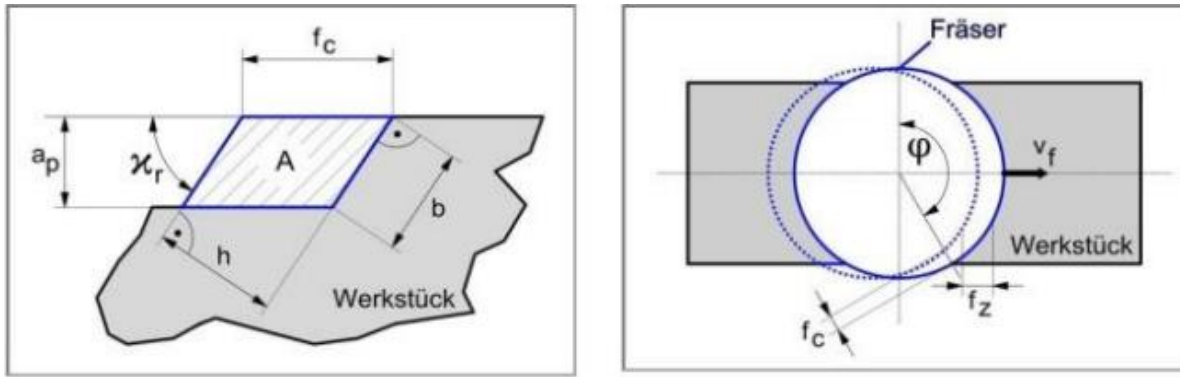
Werkzeugeingriff beim Fräsen [4]
